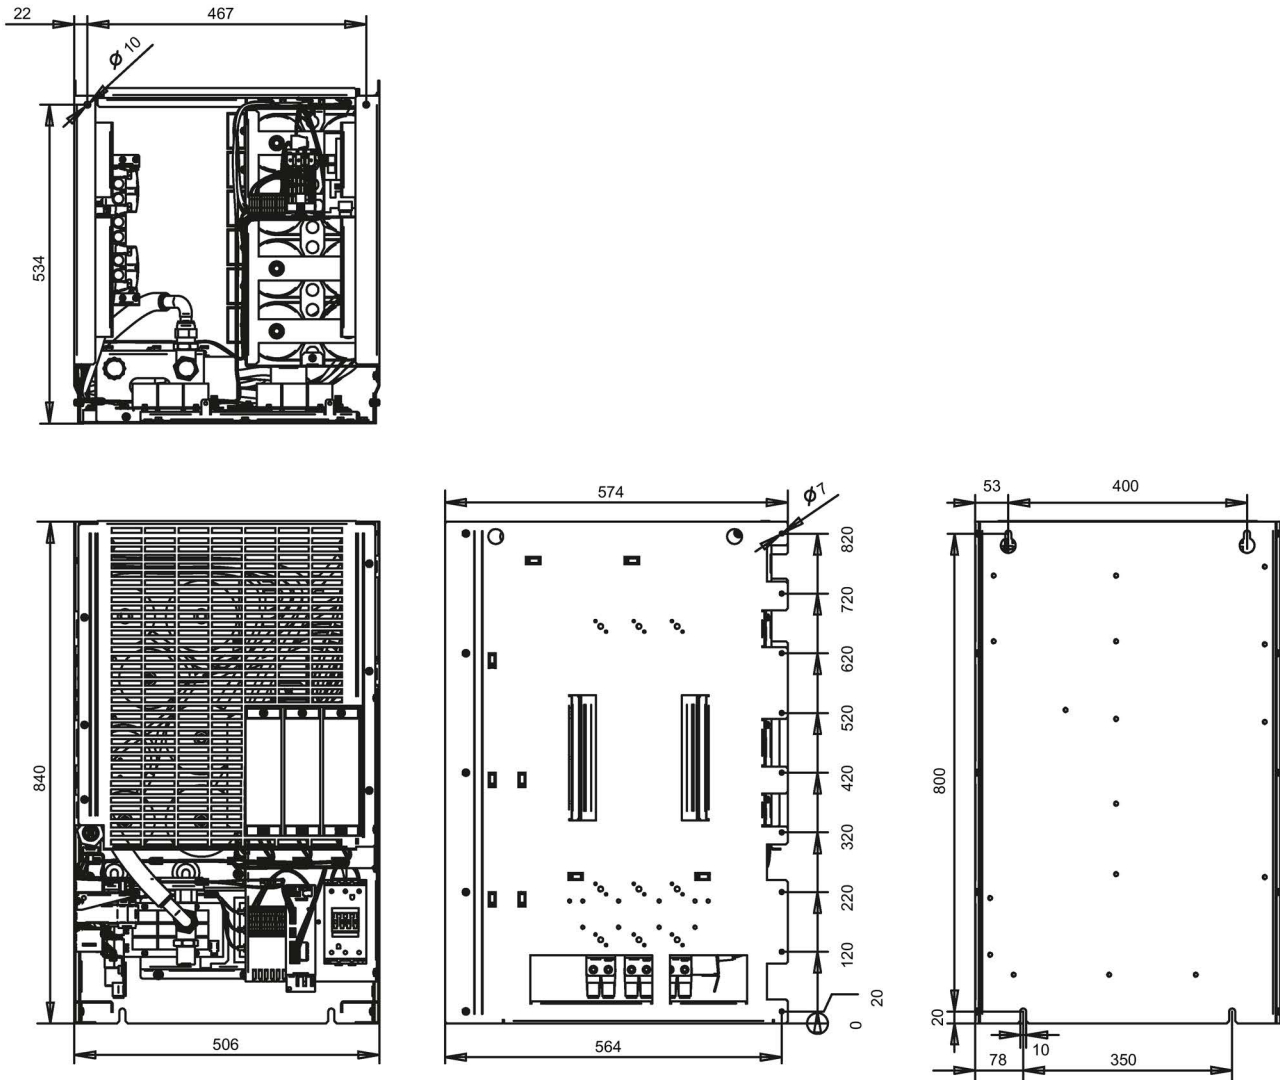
Габаритный чертеж модуля фильтра, типоразмер J1L
